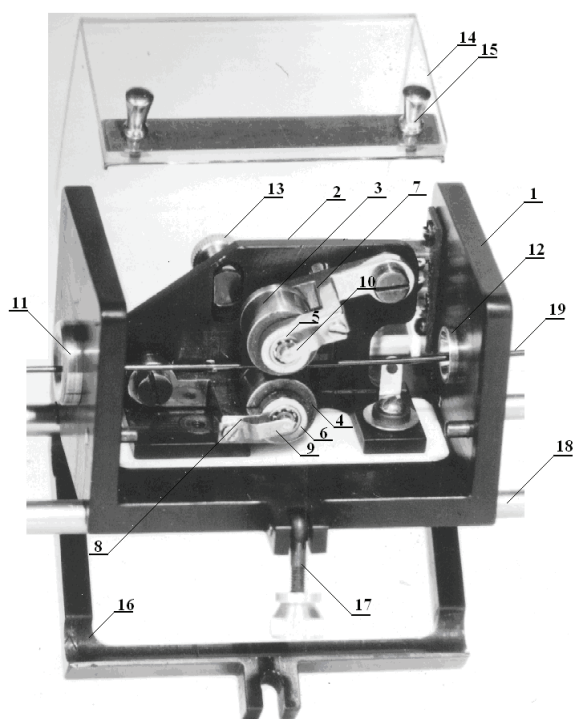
Первичный преобразователь дефектов: 1 – корпус датчика; 2 – основа для крепления рабочих элементов датчика; 3 и 4 – два свободно вращающихся ролика, выполненных из нержавеющей стали; 5 и 6 – подшипники; 7 и 8 – коромысла; 9 и 10 – скользящие контакты; 11 и 12 – направляющие втулки; 13 – концевой выключатель; 14 – изоляционная крышка; 15 – фиксаторы крышки; 16 – платформа датчика; 17 – элемент крепления датчика; 18 – рама для крепления датчика; 19 – контролируемый провод
